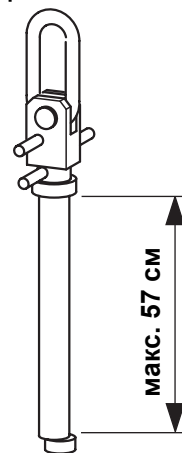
Приспособления для подвешивания для различных нагрузок
